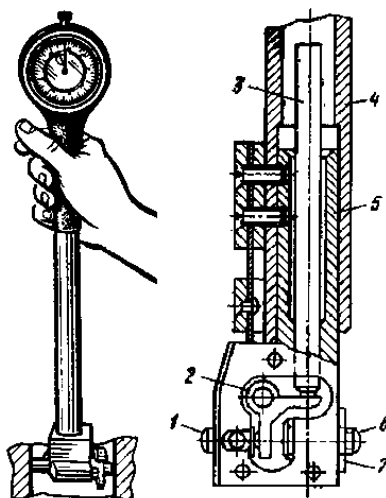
Обозначения: 1 — подвижный стержень, 2 — рычаг, 3 — шток, 4 — трубка, 5 — корпус, 6 — неподвижный стержень, 7 — контргайка
